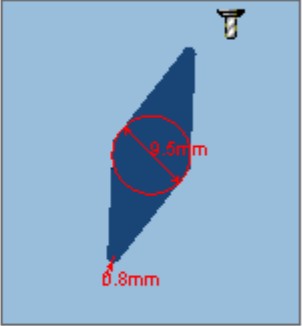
Ріжуча пластинка «VBMT 16 04 08-PR 4425»
